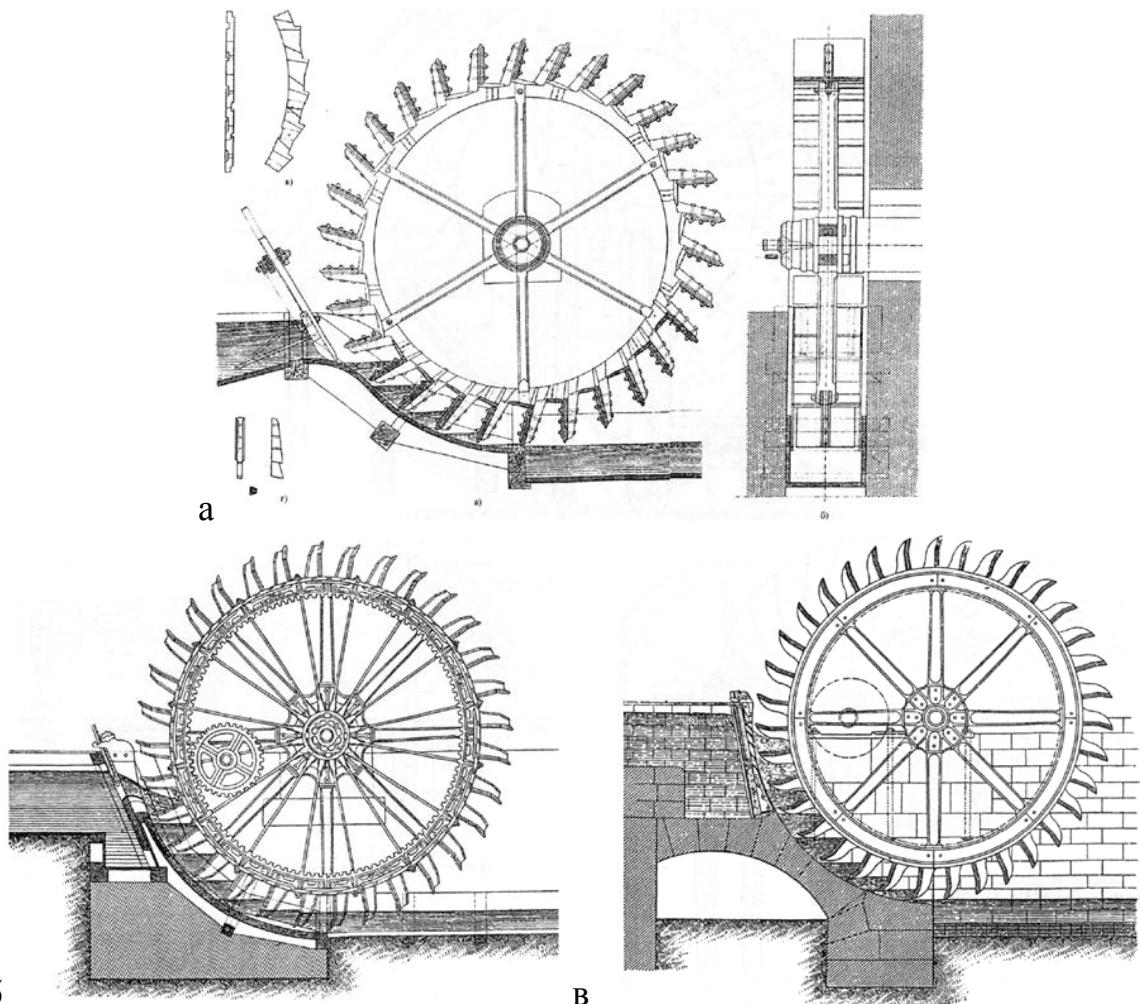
Боковые колёса с впуском воды [59]: а – ниже горизонтального радиуса, из дерева, $D = 5,34$ м; а) – вид спереди; б) – вид сбоку; в) – форма и расположение отверстий на ободе; г) – клинья, с помощью которых прикреплены лопасти к ободу колеса; б – вблизи горизонтального радиуса и с деревянным руслом; в – через щитовые отверстия и с руслом, выложенным из тёсаного камня
